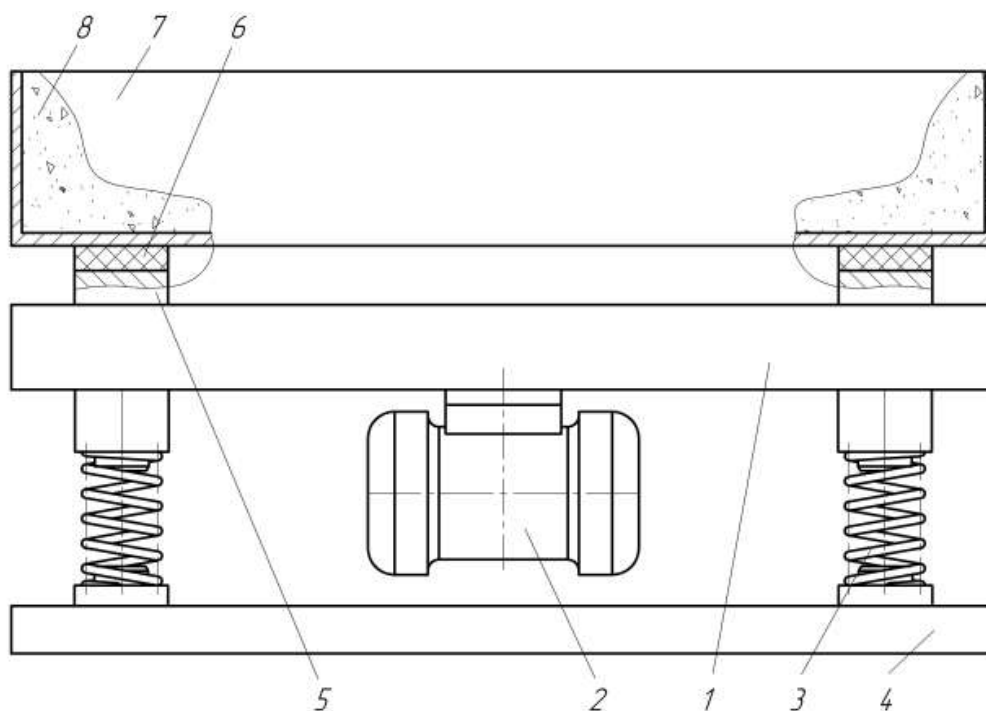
Общий вид двухмассной виброплощадки для формирования бетонных изделий
